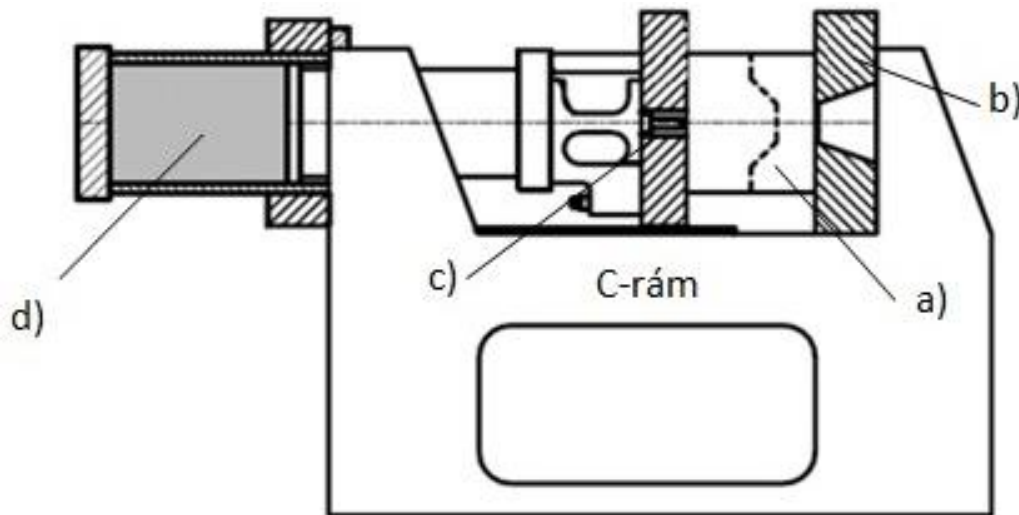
Příklad konstrukce vodícího pouzdra [6]
